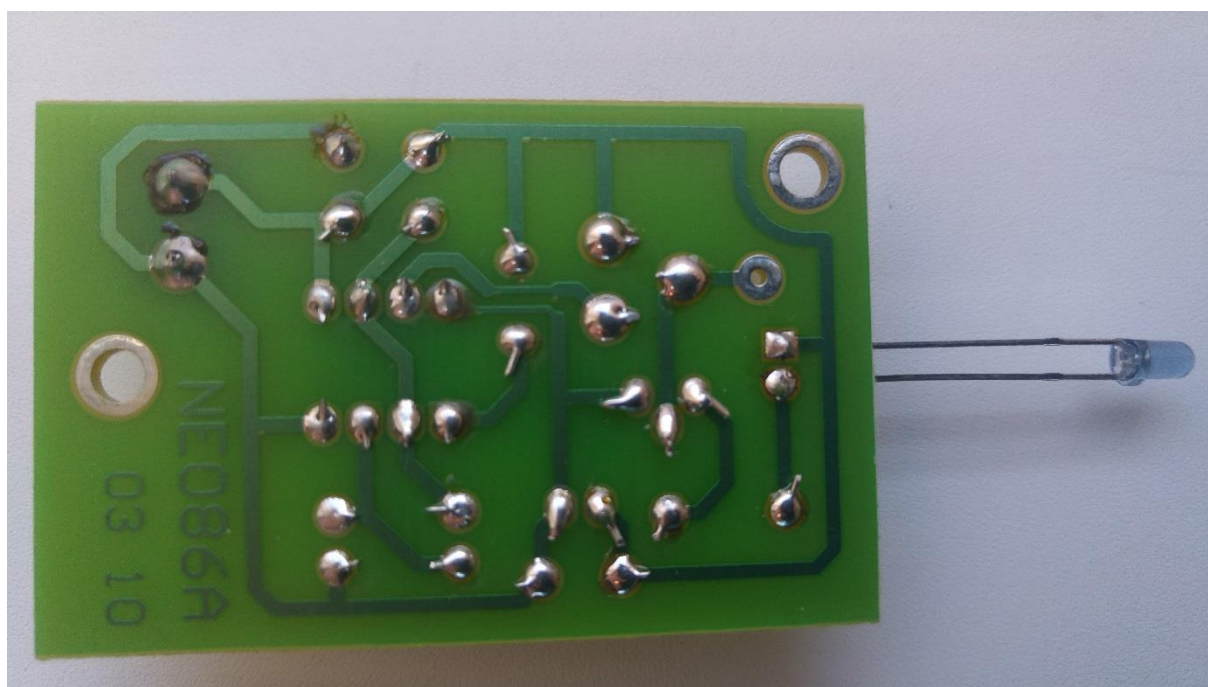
Model prijímača – pohľad na vrchnú časť PCB
